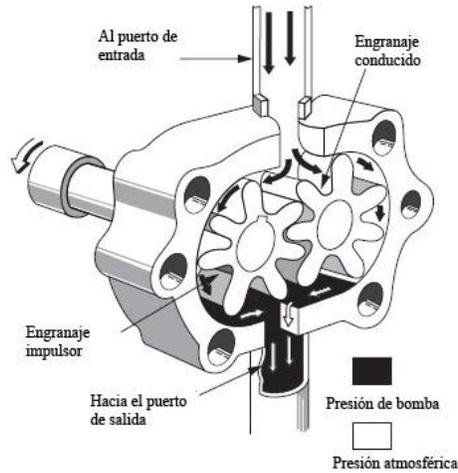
Bomba Rotativa de Engranajes Externos ¹
